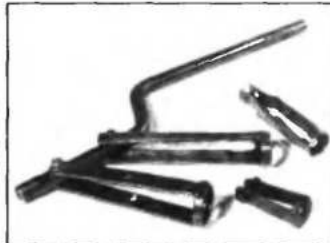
Рычажное приспособление для разборки/сборки пружин клапанов, применяемое без снятия головки с блока цилиндров
